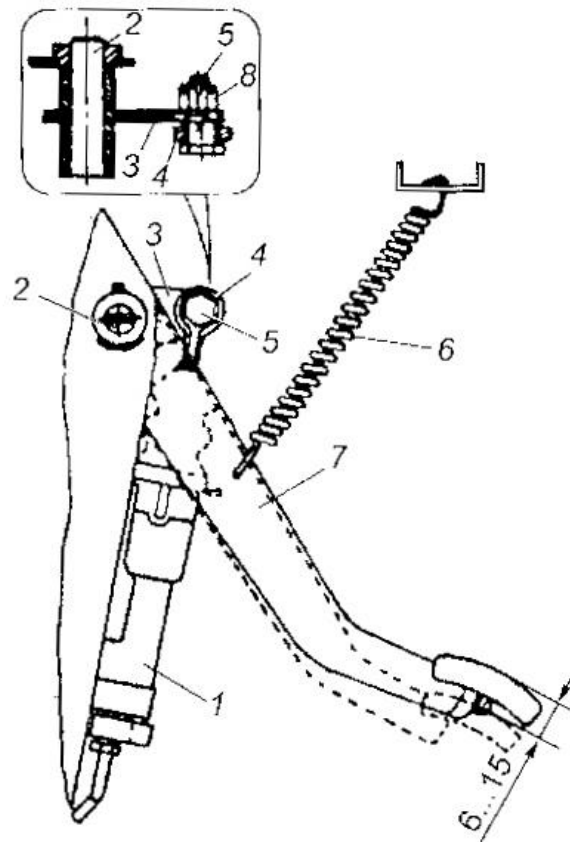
Перевірка та регулювання вільного ходу педалі зчеплення: 1 - головний циліндр зчеплення; 2 - вісь педалі; 3 - важіль штовхача; 4 - пружина штовхача; 5 - ексцентриковий палець; 6 - пружина; 7 – педаль; 8 – гайка.
